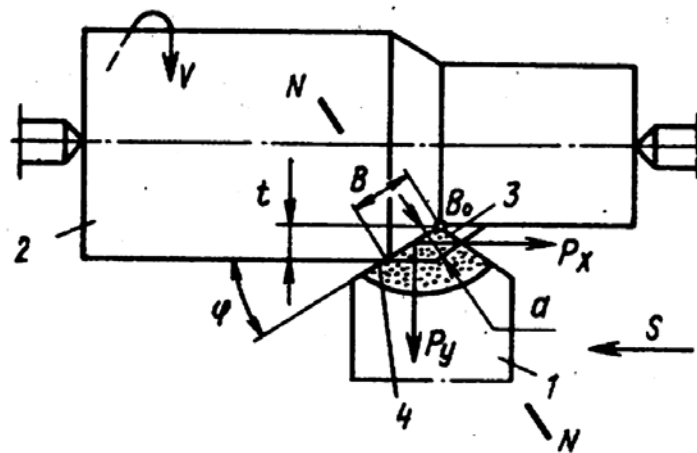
Схема обработки: 1 – резец; 2 – обрабатываемая деталь; 3 – сечение среза; 4 – главное режущее лезвие резца
